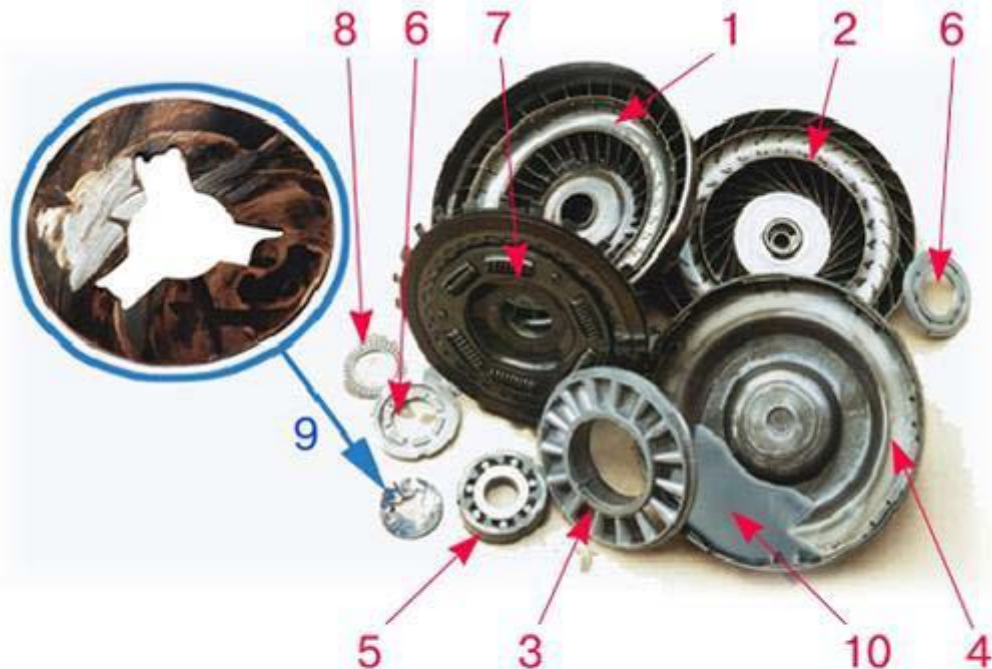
Детали гидротрансформатора: 1 - насосное колесо; 2 - турбинное колесо; 3 - колесо реактора; 4 - часть корпуса ГДТ; 5 - муфта свободного хода реактора; 6 - крышки муфты свободного хода; 7 - поршень блокировки ГДТ; 8 - упорный подшипник реактора; 9 - упорная шайба турбинного колеса; 10 - остатки рабочей жидкости с продуктами механического износа деталей.
